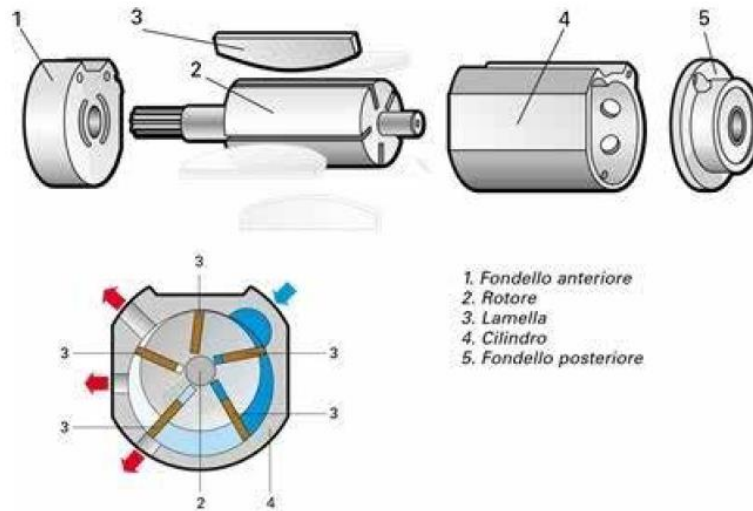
Struttura del motore pneumatico a palette [12]
